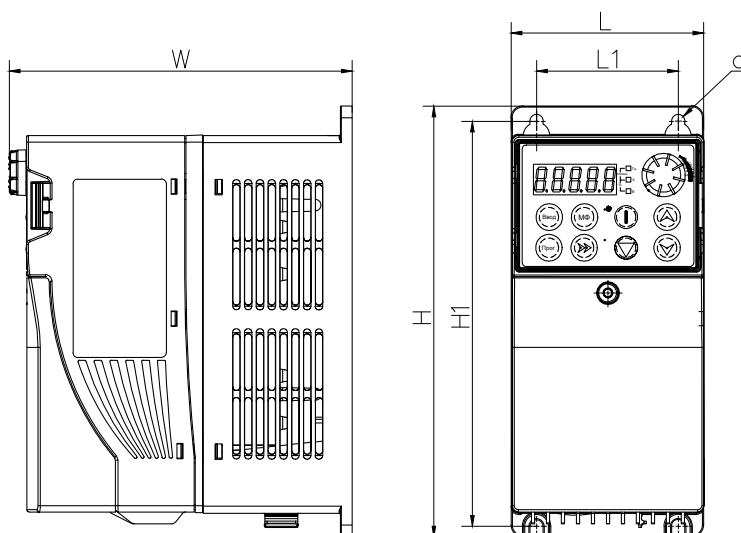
Габаритные и установочные размеры преобразователя (габарит 1)
